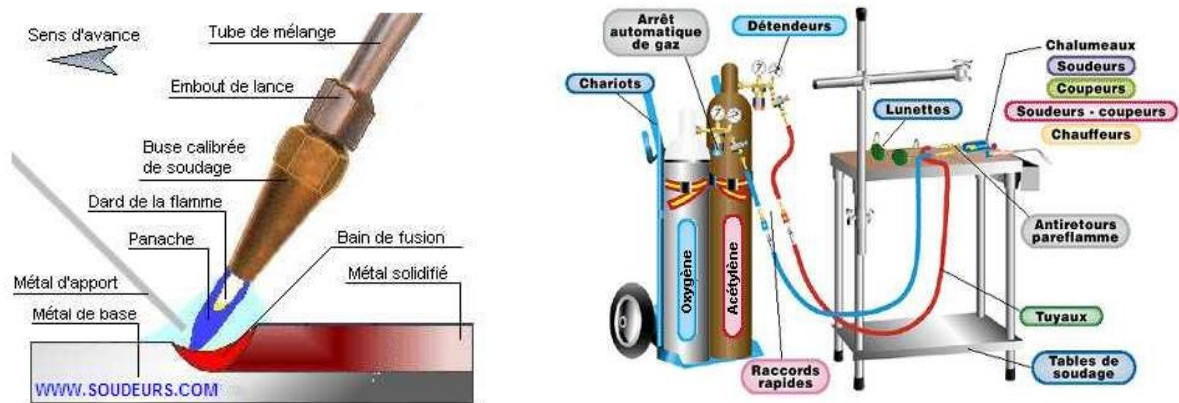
Principe de Soudage oxygaz et le croquis didactique du procédé de soudage a la flamme oxyacétylénique [17]
